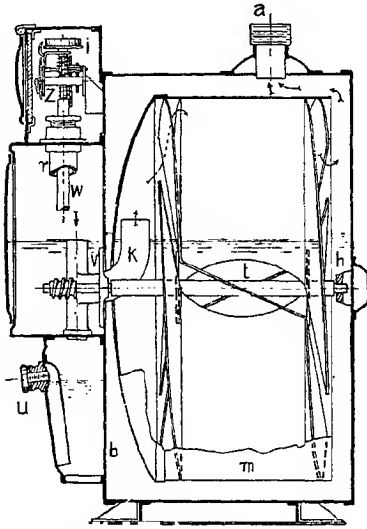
Schnitt durch den Gasmesser von BESSIN & CO., Berlin.
